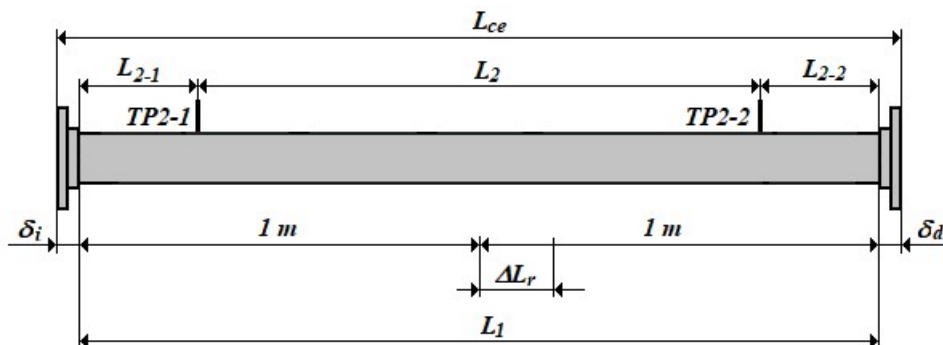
Prototipo TC-02-(0.4/2). Dimensiones de la cámara de expansión.
